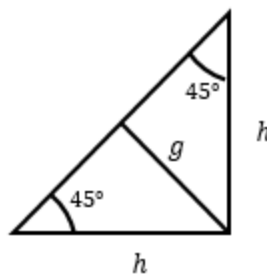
Longitud g de la garganta de soldadura. Fuente: Propia.
